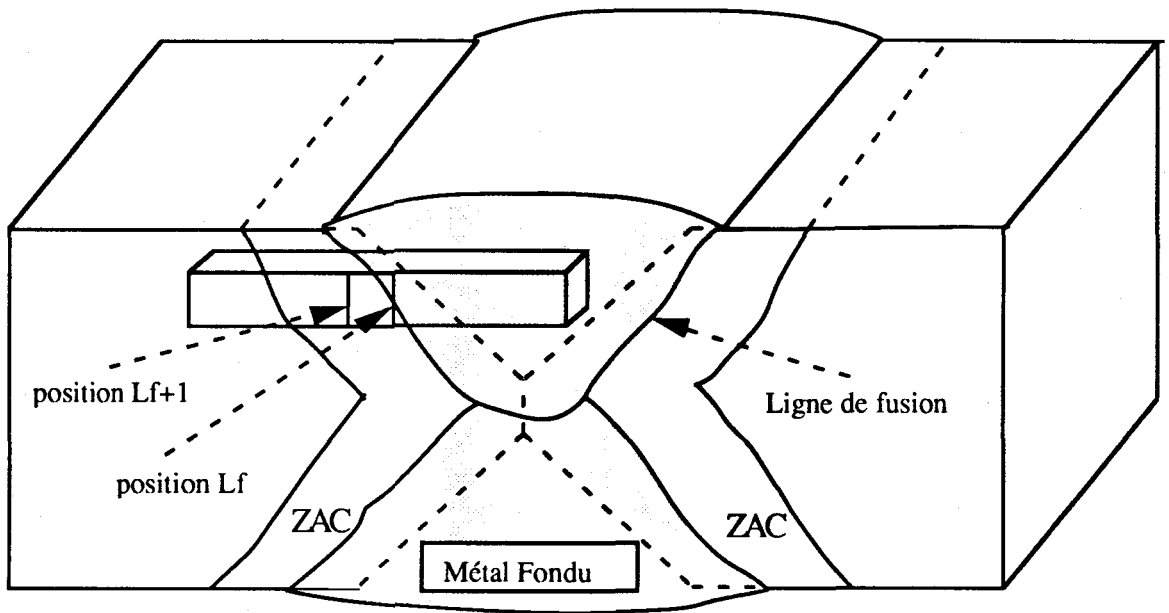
Schéma de prélèvement des éprouvettes Charpy dans un joint soudé
